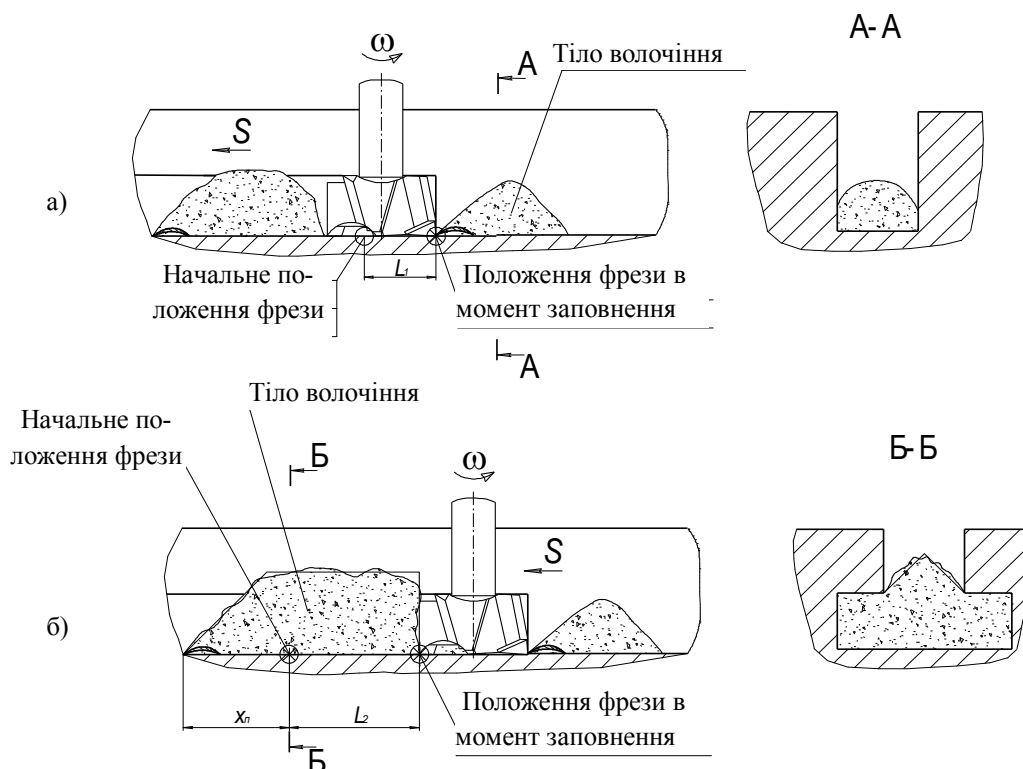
Схема заповнення стружкою пазів при їх фрезеруванні:
